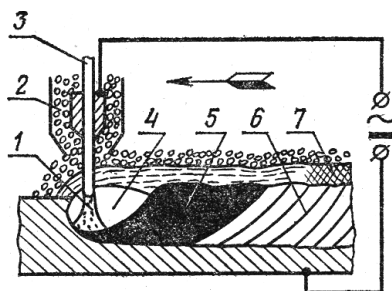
Сварка под флюсом: 1 — электрическая дуга; 2 — флюс; 3 — электродная проволока; 4 — газовое пространство; 5 — ванна расплавленного металла; 6 — сварной шов; 7 — шлаковая корка
